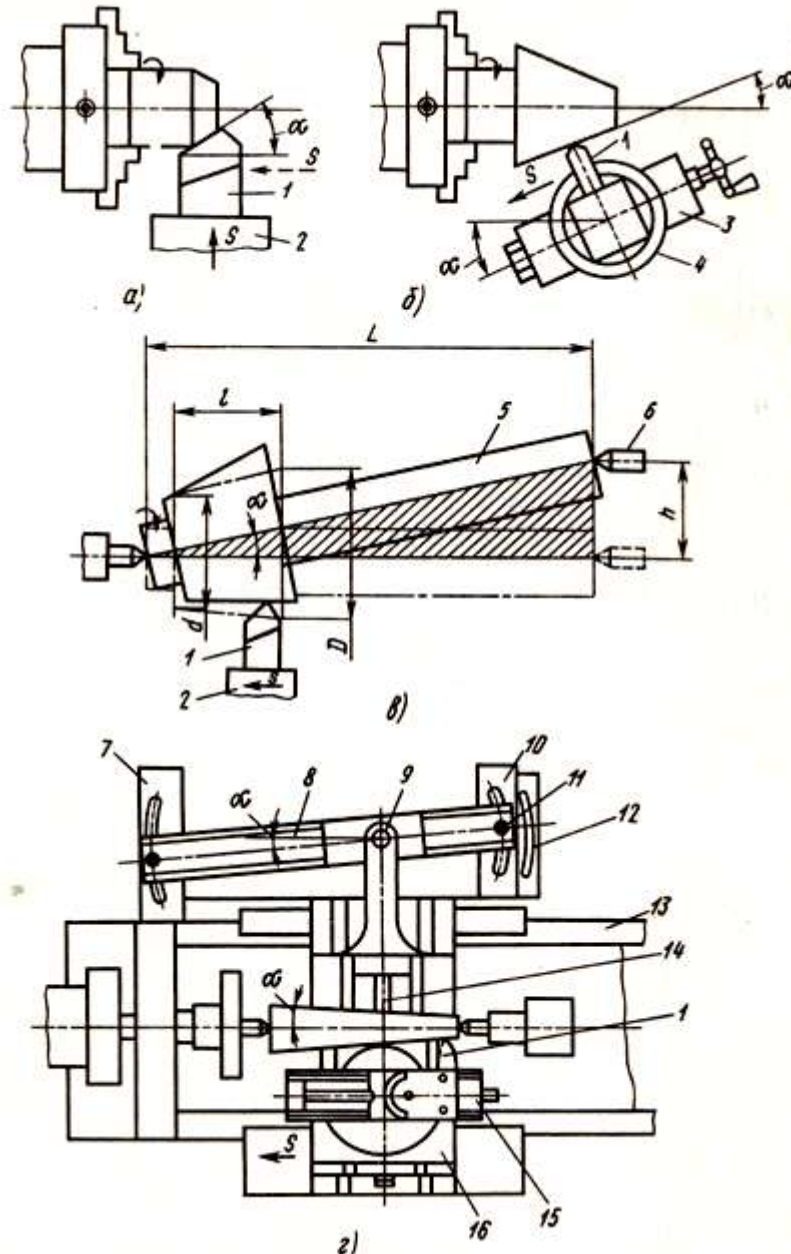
Схеми обробки конічних поверхонь на токарних верстатах:
